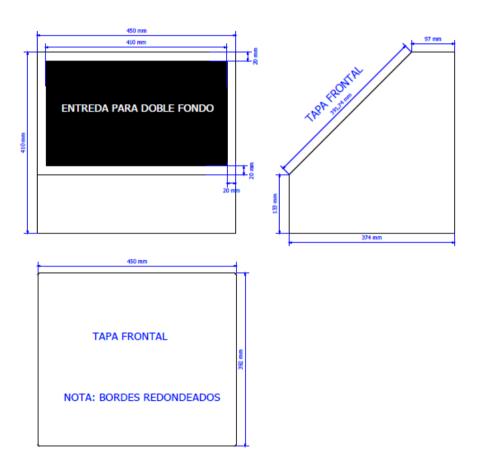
Dimensiones módulo DMP LAB INDUSTRY.
